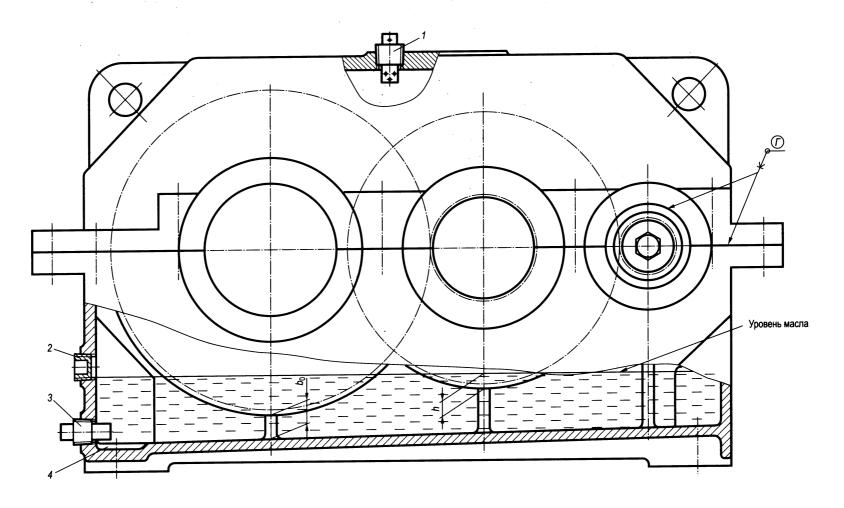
Двухступенчатый редуктор по развернутой схеме с погружением быстроходного колеса в масляную ванну: 1 – заливная пробка-фильтр; 2 – контрольная пробка ; 3 – сливная пробка с магнитом; 4 – приямок ($h \cong 5m$; $b_0 \ge 2h$)
